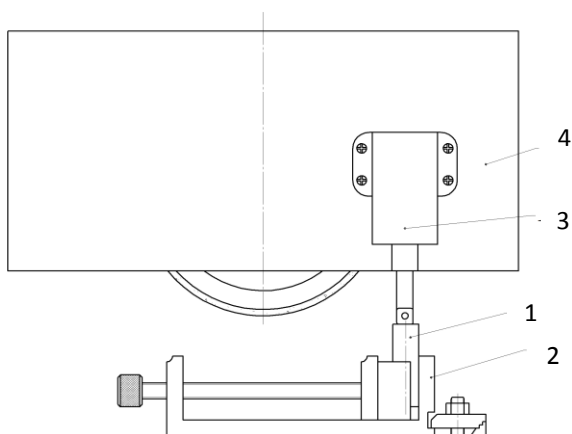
Схема установки для УЗ релаксации ТОН в ПС заготовки: 1 – заготовка, 2 – приспособление, 3 – УЗ волновод, 4 – кожух шлифовального круга
